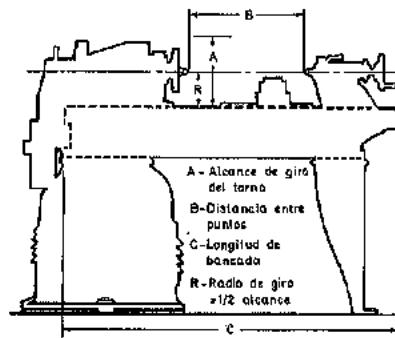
Modo de especificar las medidas de un torno (South Bend Lathe Works).
